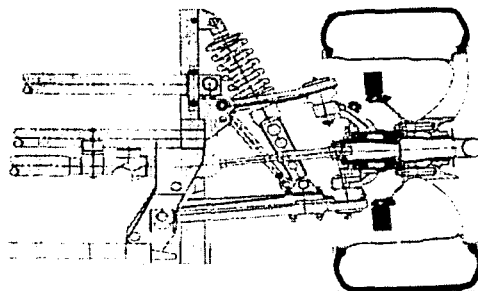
Suspensión con eslabonamientos planos en paralelo
